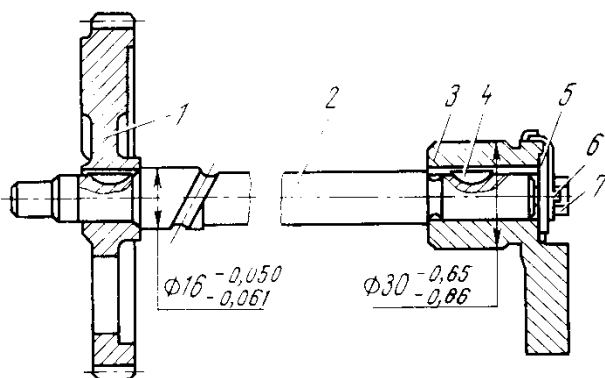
Балансирующий механизм в сборе: 1 — шестерня балансирующего вала; 2 — балансирующий вал; 3 — противовес; 4 — сегментная шпонка; 5 — шайба балансирующего вала; 6 — стопорная шайба; 7 — стопорный болт
